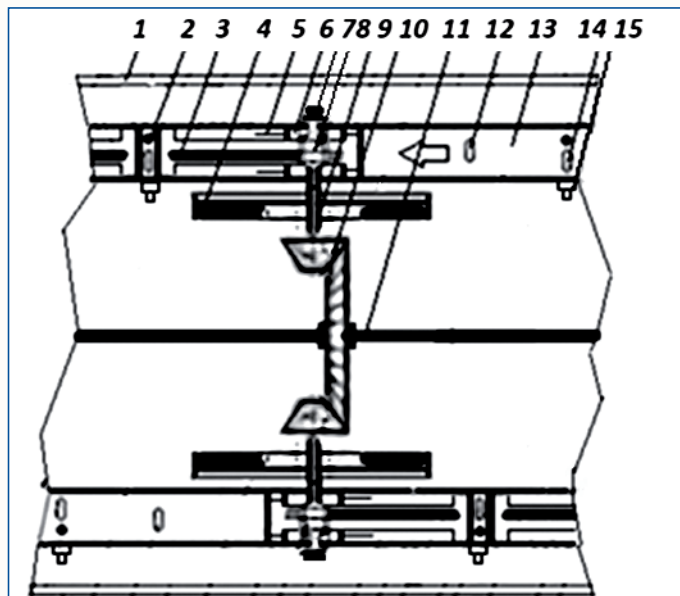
Схема двигателя с последовательно-оппозитным расположением поршней: 1 - теплоизолированный ресивер сжатого воздуха; 2 - газовый инжектор; 3 - нижняя зубчатая рейка; 4 - маховик; 5 - шток гидравлического тормоза; 6 - блок управления и фиксации мертвой точки; 7 - щёточные контакты; 8 - РШМ; 9 - вал отбора мощности; 10 - редуктор; 11 - гребной вал; 12 - промежуточный клапан; 13 - блок цилиндров; 14 - впускной-выпускной клапан; 15 - лазерная свеча зажигания
